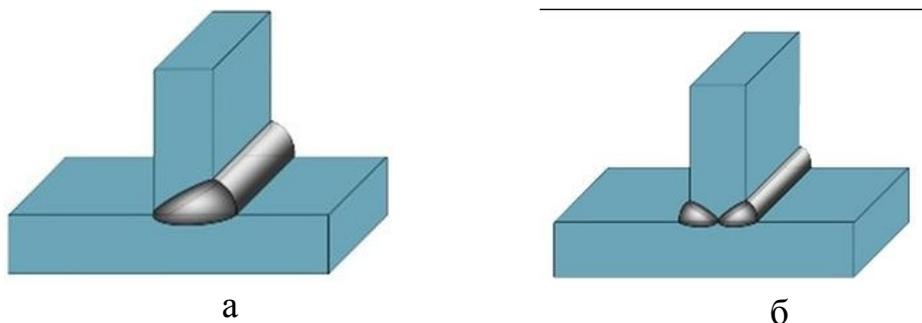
Образец выполнения сварных швов по типу выполнения.
